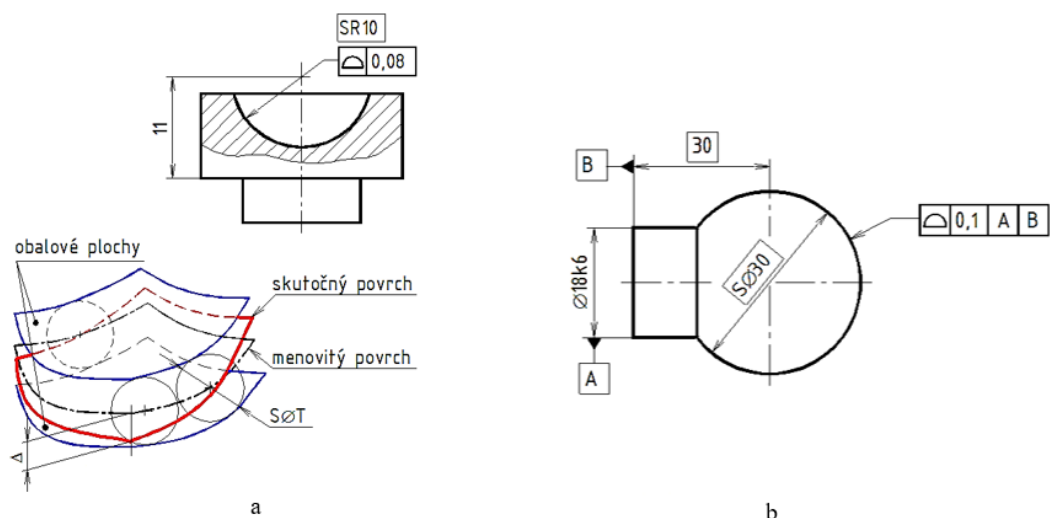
Tolerancia profilu ľubovoľného obrysu (Čillík, 2012)
